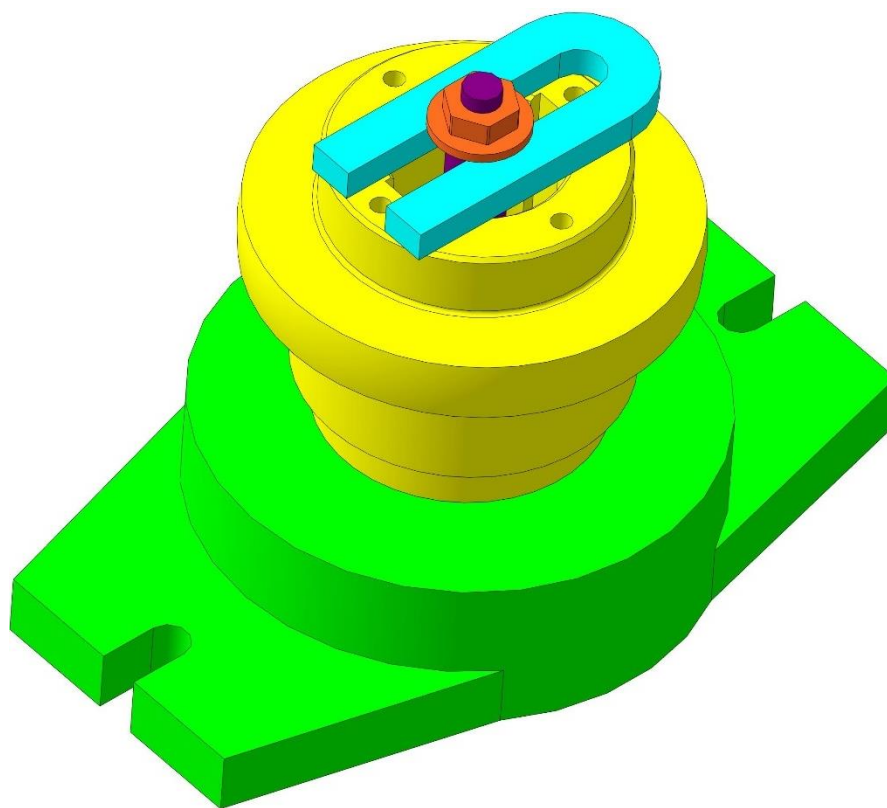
Розроблений верстатний пристрій із деталлю
